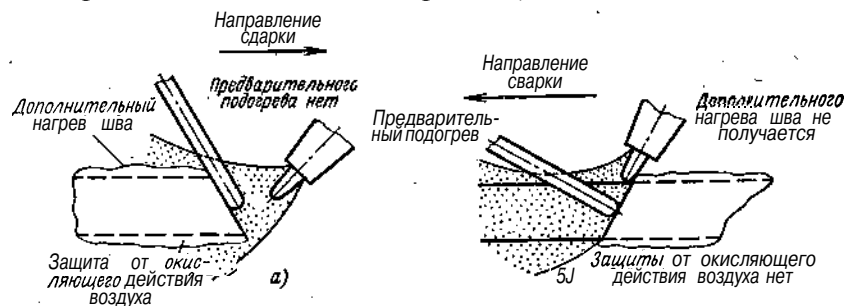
Правый (а) и левый (б) способы газовой сварки
